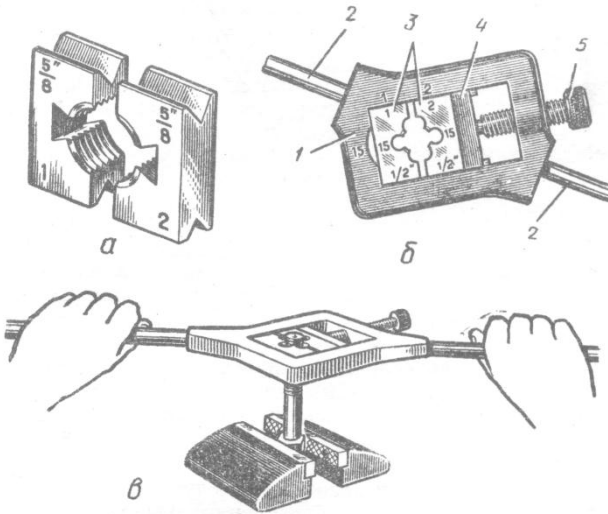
Розсунні (призматичні) плашки: а – загальний вигляд; б – закріплення в крупі; в – нарізування різьби
